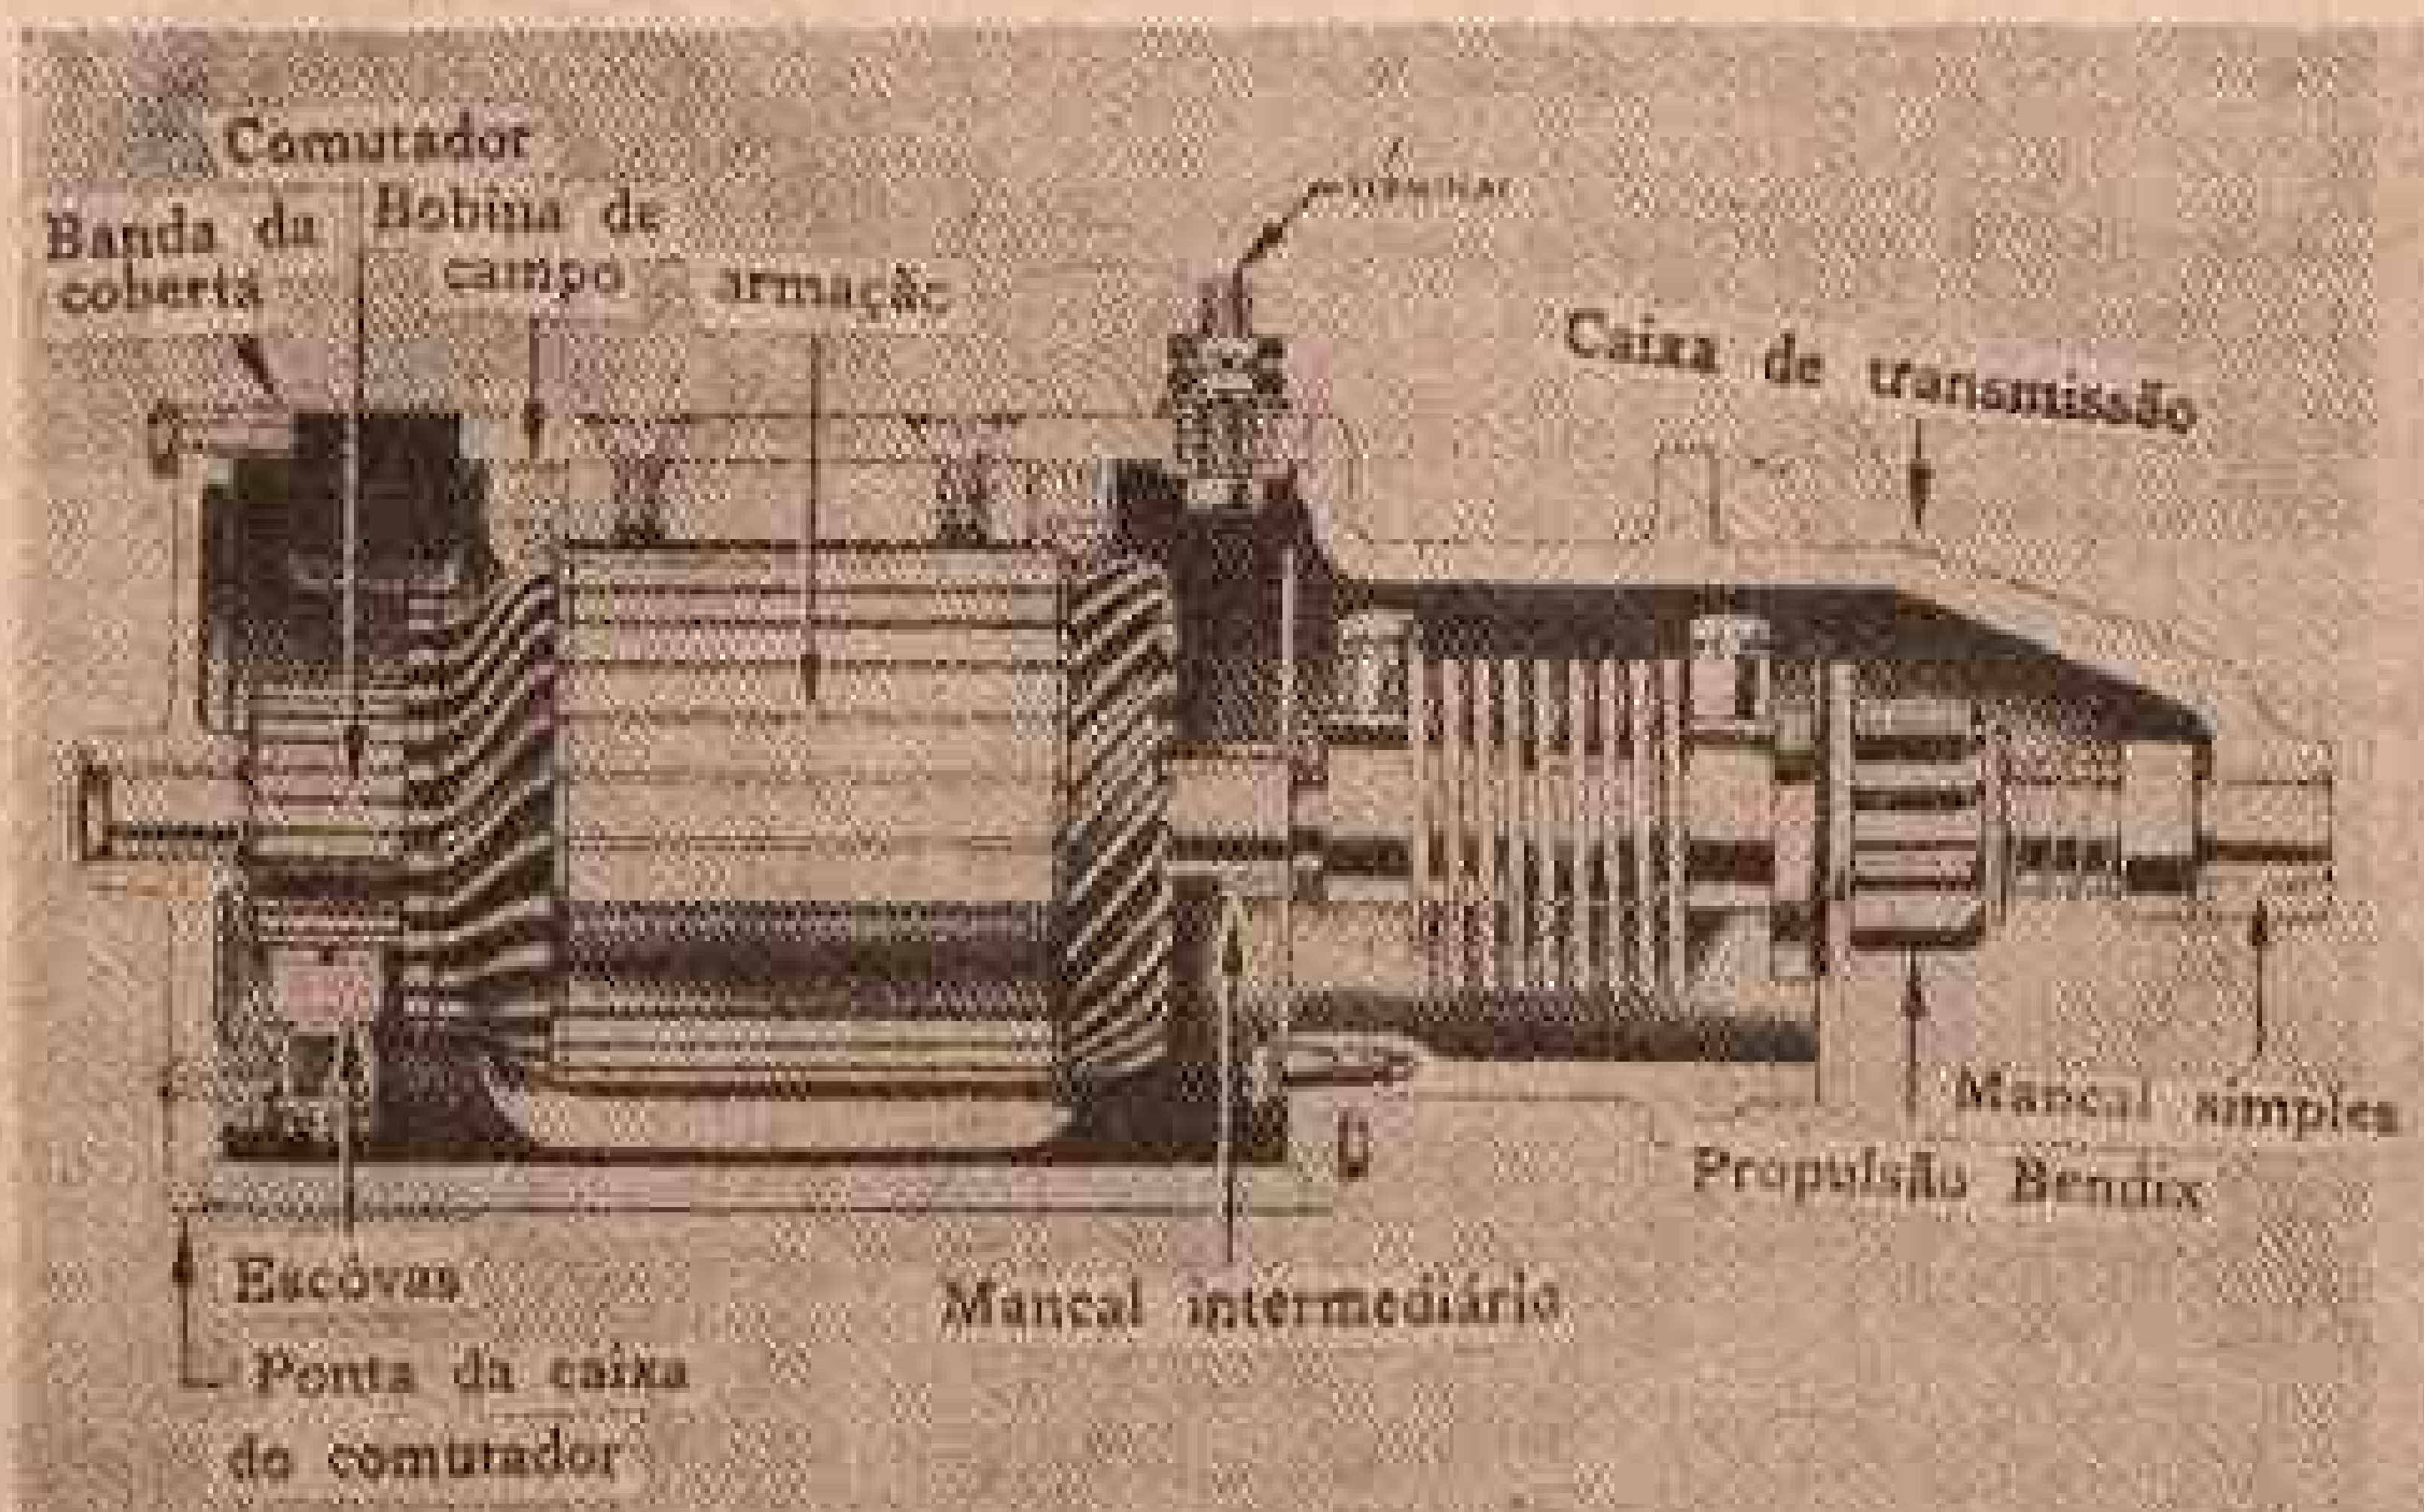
Corte vertical de um motor de arranco com propulsão Bendix.
